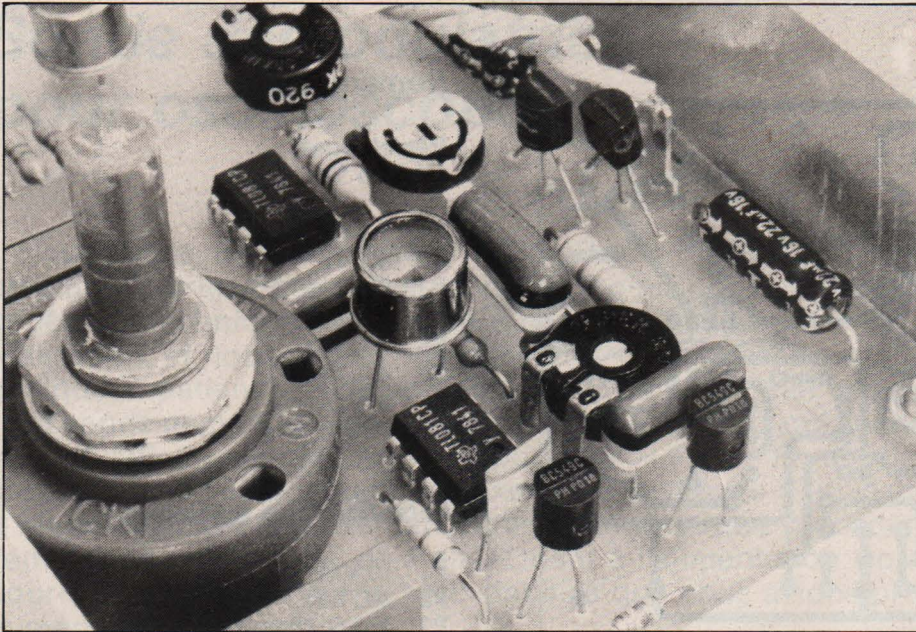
La photodiode est soudée en conservant toute la longueur des pattes.
